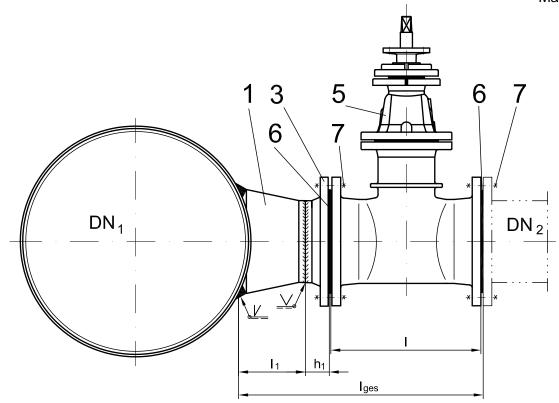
Abzweig von Stahlleitung für Anbohrung unter Druck, Variante 1, Ausführung A (Ausführung mit Reduzierstück (Pos. 1); DN₂ ≥ DN 100)
